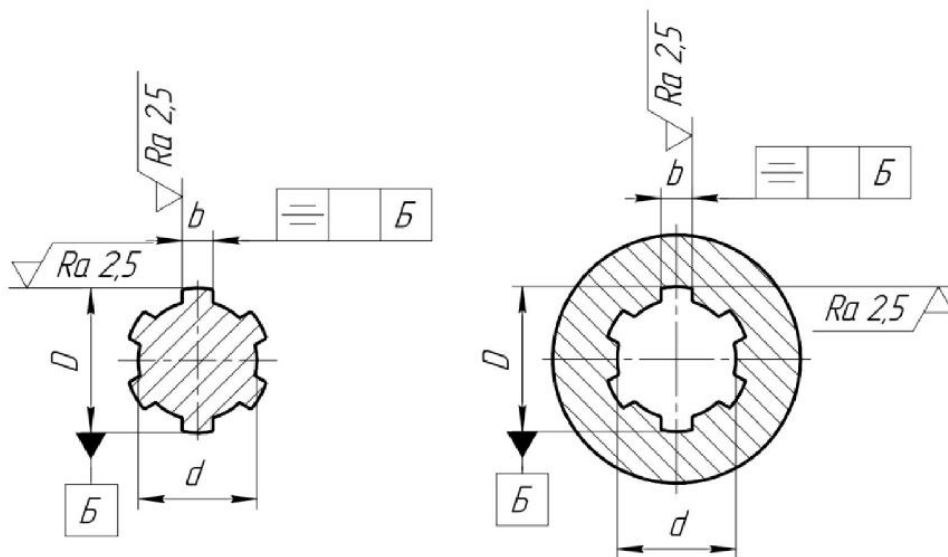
Базові поверхні, чистота обробки та допуски форм і розташування поверхонь шліцьового прямобічного з'єднання при центруванні за зовнішнім діаметром
